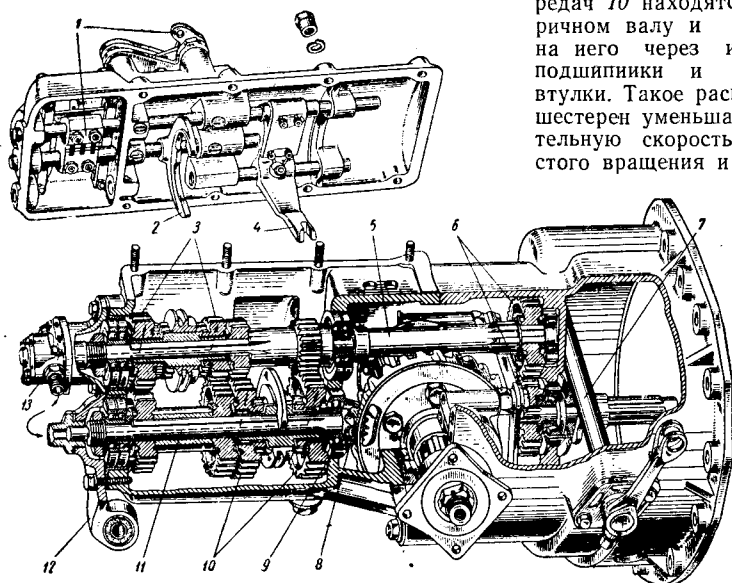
Четырехступенчатая коробка передач гоночного автомобиля Купер (рабочий объем 2,5 л) с задним расположением двигателя:
